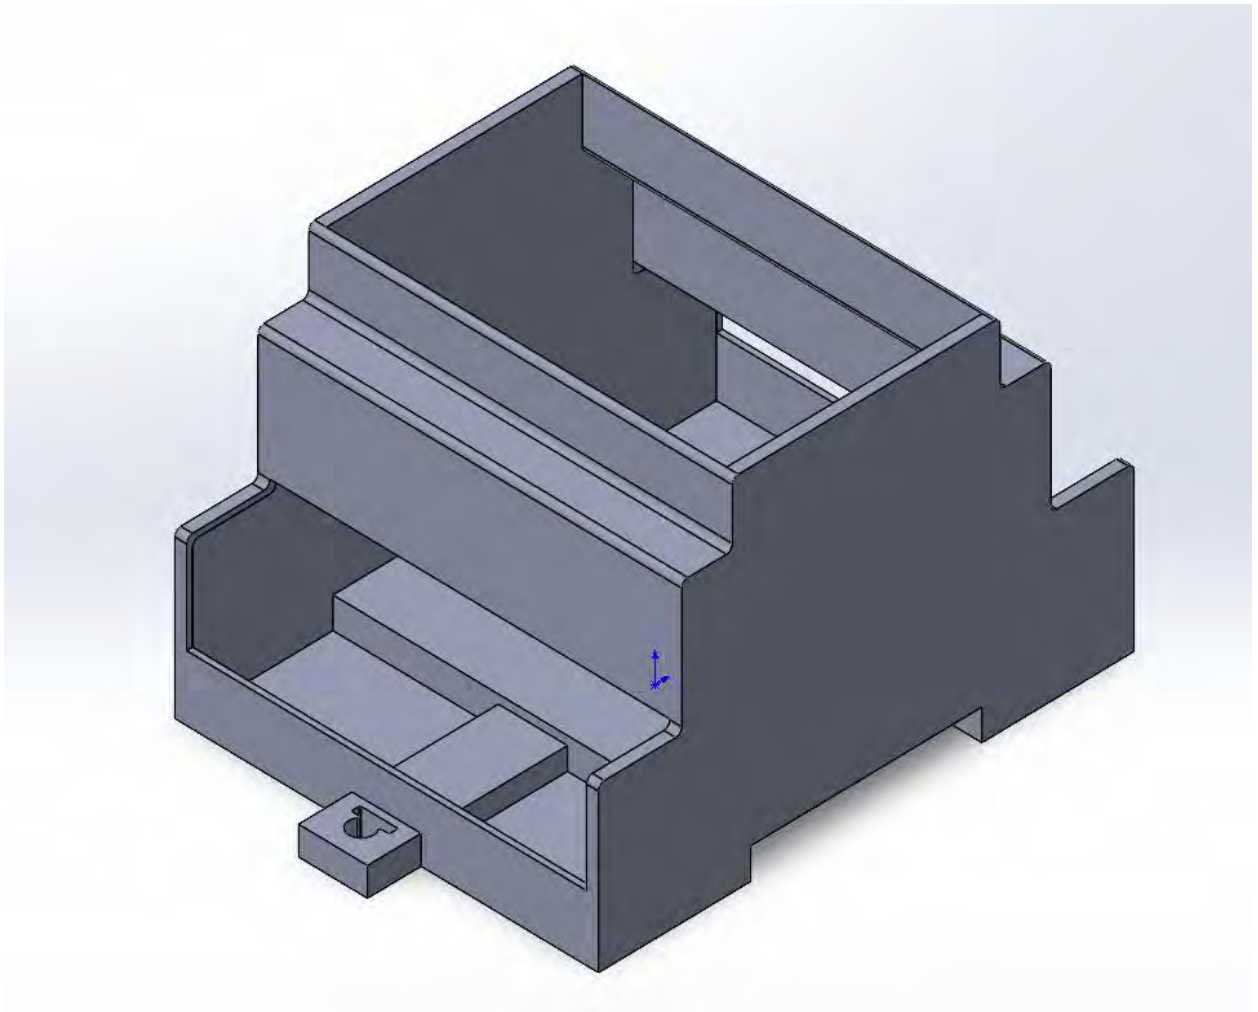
Зовнішній вигляд корпусу пристрою
